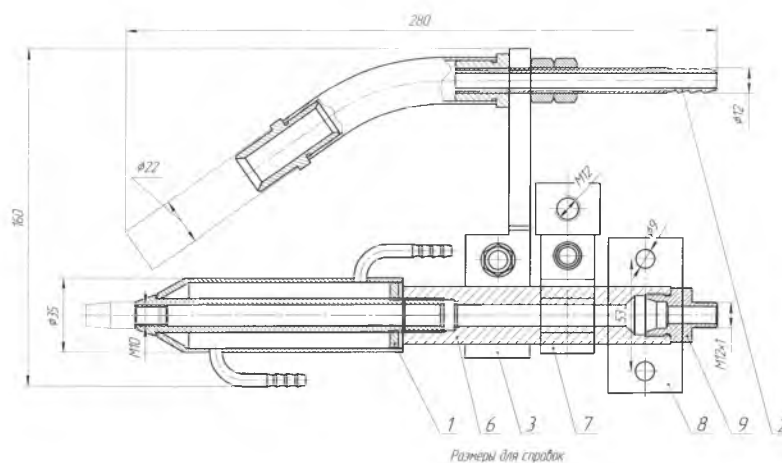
Горелка для автоматической сварки в среде защитных газов:
